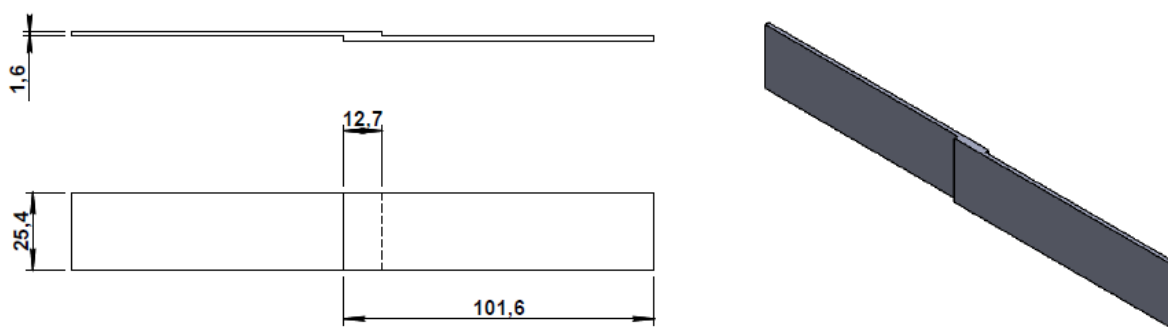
Junta single-lap com dimensões padronizadas pela ASTM D 1002-01.
